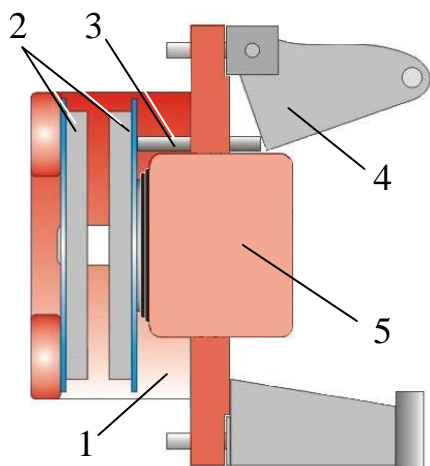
Схема механизма стояночного тормоза для дискового тормозного механизма: 1 – плавающая скоба; 2 – тормозные колодки; 3 – толкатель; 4 – рычаг; 5 – рабочий тормозной цилиндр
